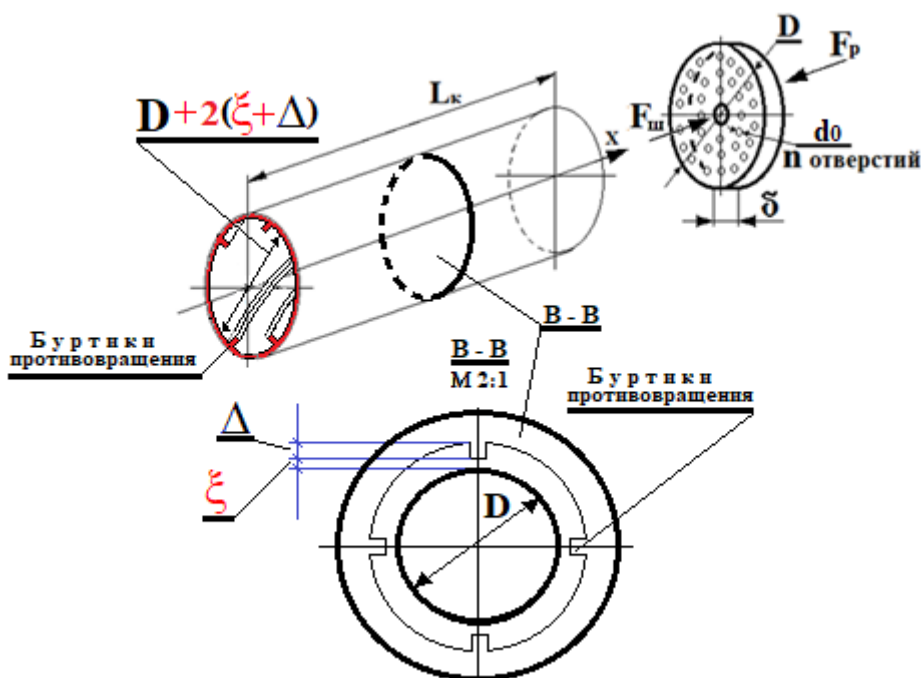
Геометрические параметры цилиндрического корпуса и выходной решетки экструдера
